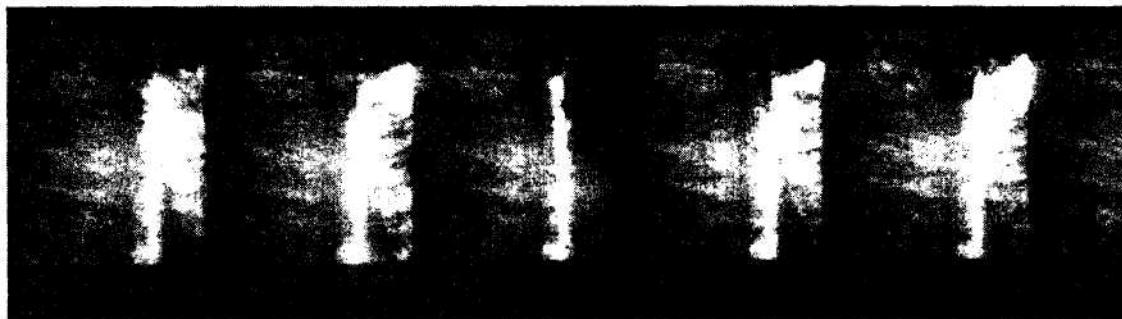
Фрагмент кінострічки зйомки зношування твердосплавного інструменту BK8 під час різання жароміцної сталі ЕИ787 (x4)
